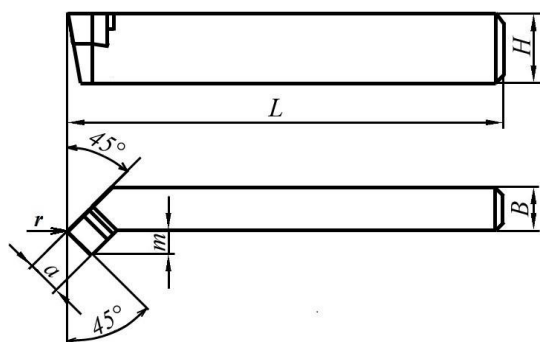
Резец токарный проходной, отогнутый с пластинками из твердого сплава (ГОСТ18877-73)
